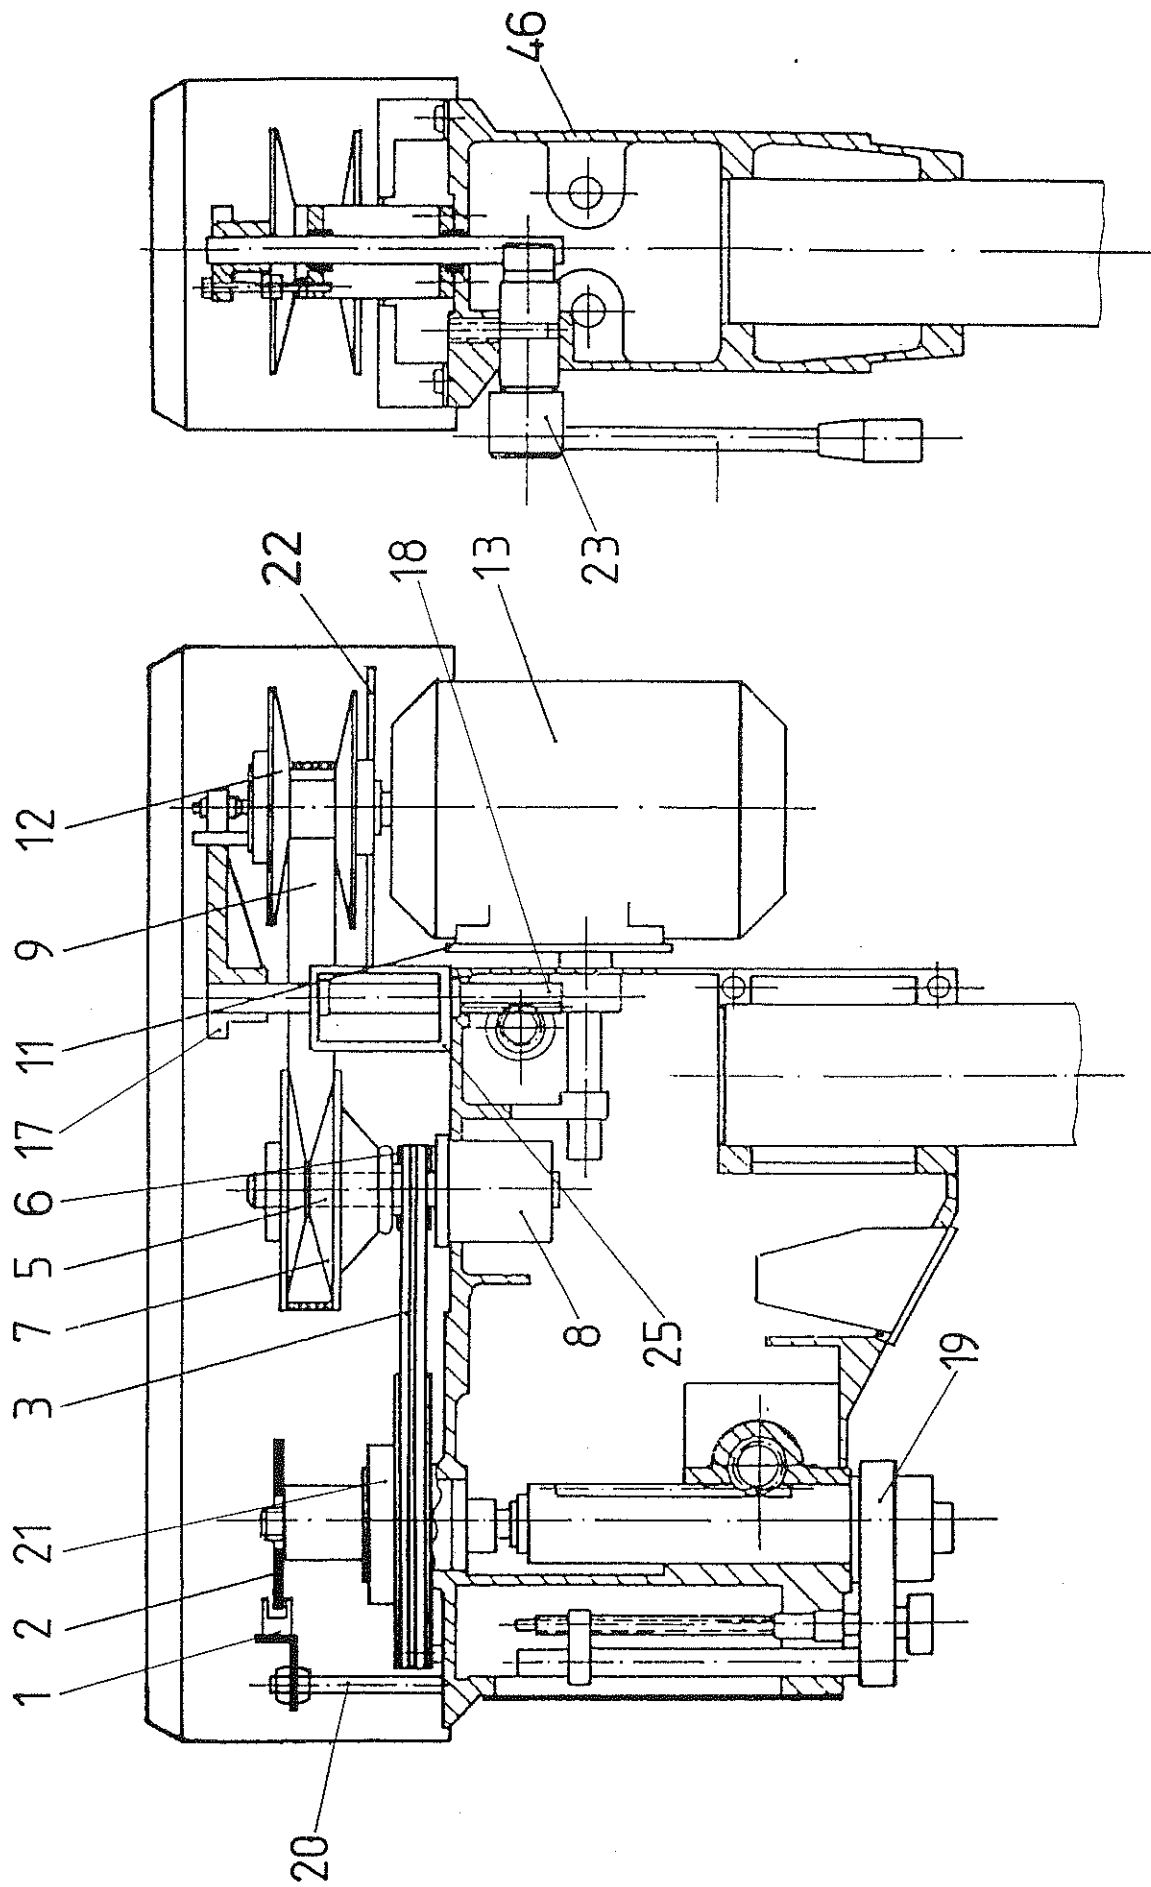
/figure 6:Bohrkopf / drilling head 25 ST
